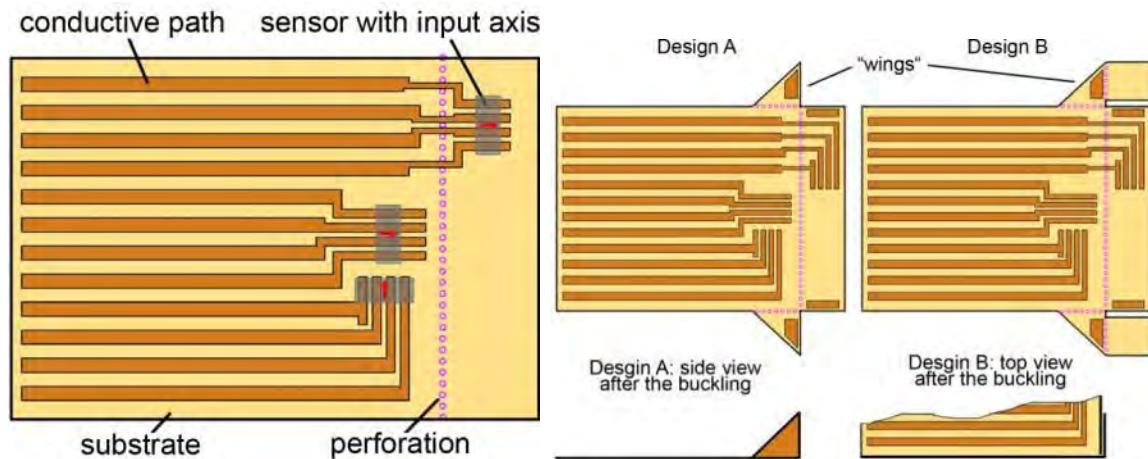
FaltFlex™ Design – Erzeugung einer dreidimensionalen Messzelle durch Faltechniken; links: Prinzip, rechts: zwei beispielhafte Designs
